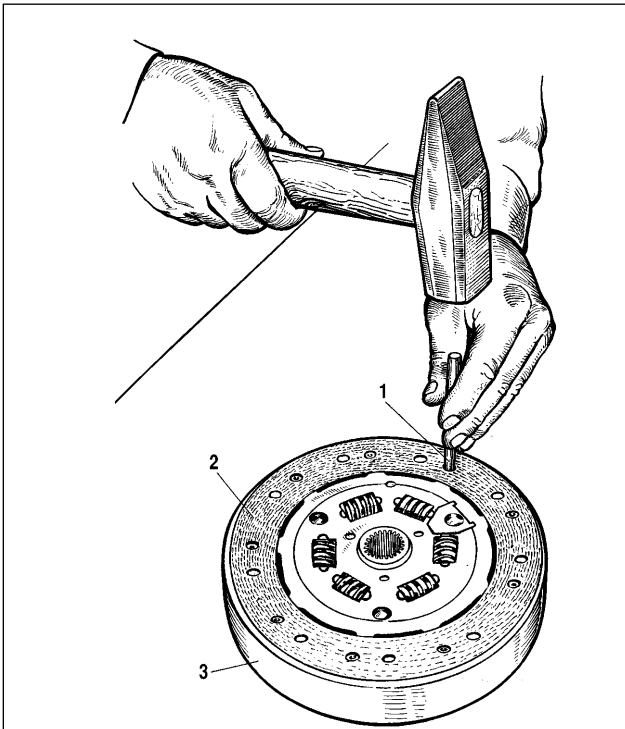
Remplacement des garnitures du disque d'embrayage:
